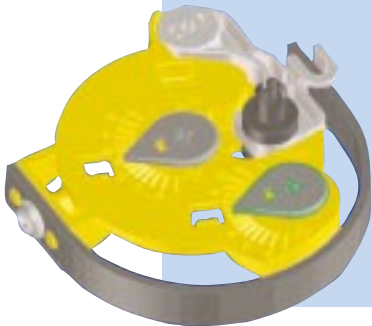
CAD-Zeichnung des V6-TC-Elementes
